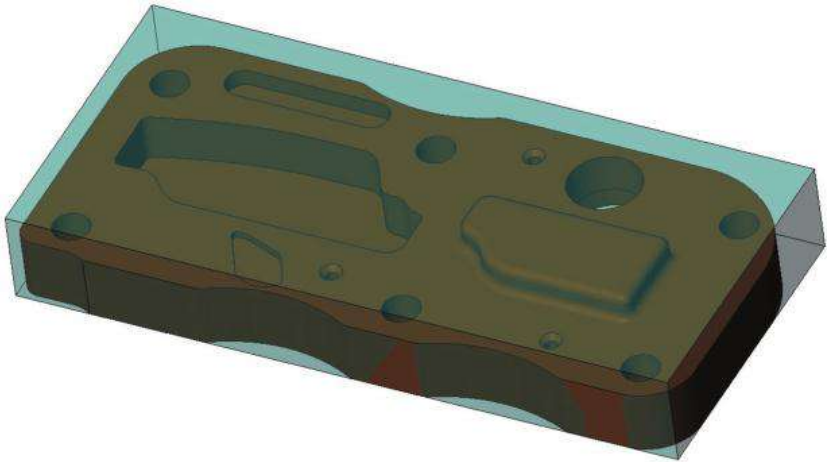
Заготовка у вигляді паралелепіпеда
